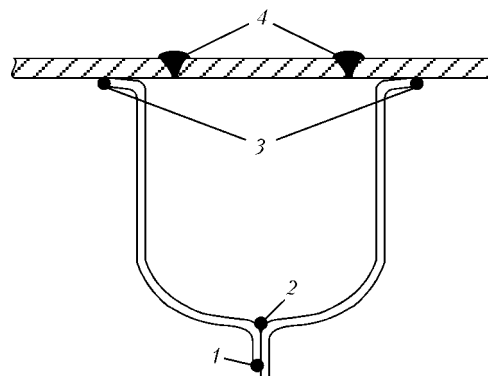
Принципиальная схема УГС: 1 — трехслойный шов, формируемый под водой с применением механизированной сварки самозащитной порошковой проволокой; 2 — дополнительный шов, выполняемый после осушения УГС электродами УОНИИ-13/45Р; 3 — монтажный угловой шов, выполненный на стапеле при подготовке УГС; 4 — многопроходный стыковой шов, выполняемый в сухих условиях при соединении донной и бортовой части суперблоков кессона
